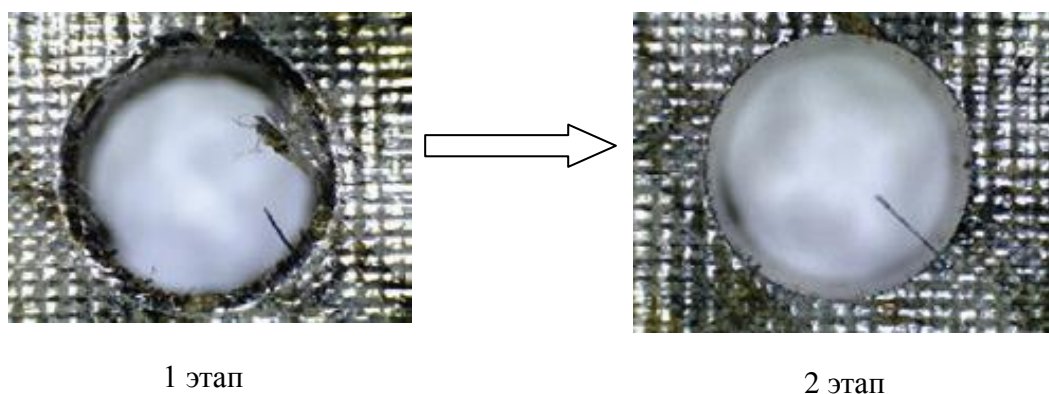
Качество отверстий при двухстадийной обработке двумя инструментами
